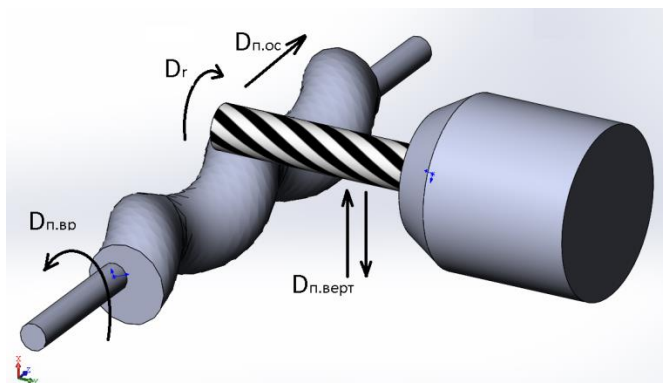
Схема обработки винтового ротора осевым инструментом.
